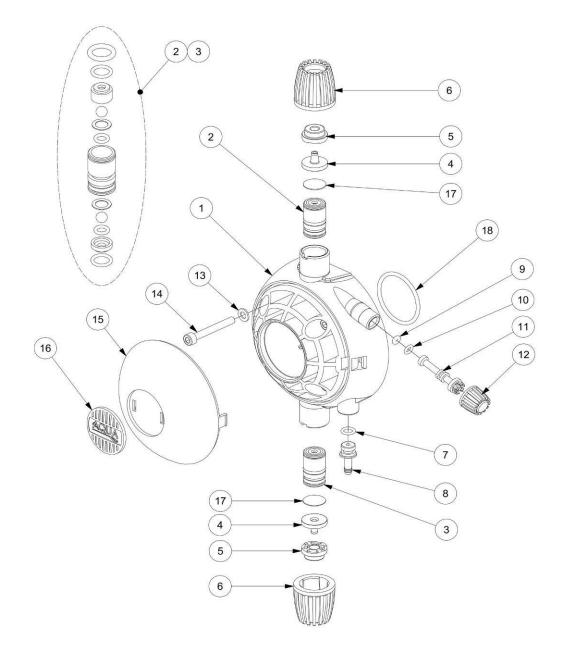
SERIE HC 999 - Esploso / Description / Explose / Dibujo / Explosionszeichnung /Чертеж
